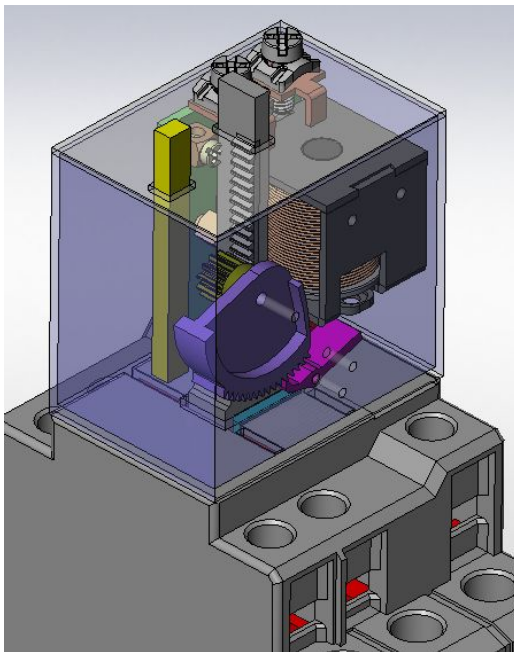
Desenho CAD do MRM acoplado ao contator de menor largura.
